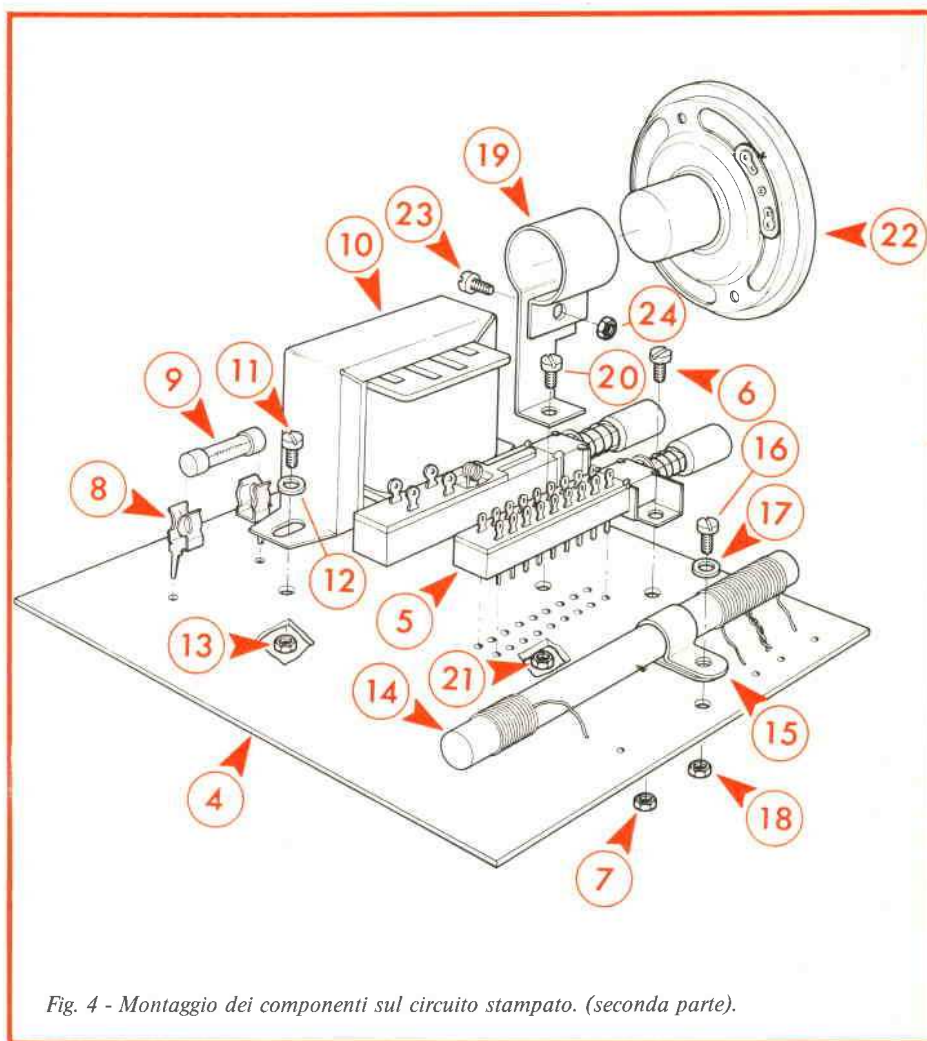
Montaggio dei componenti sul circuito stampato. (seconda parte).
